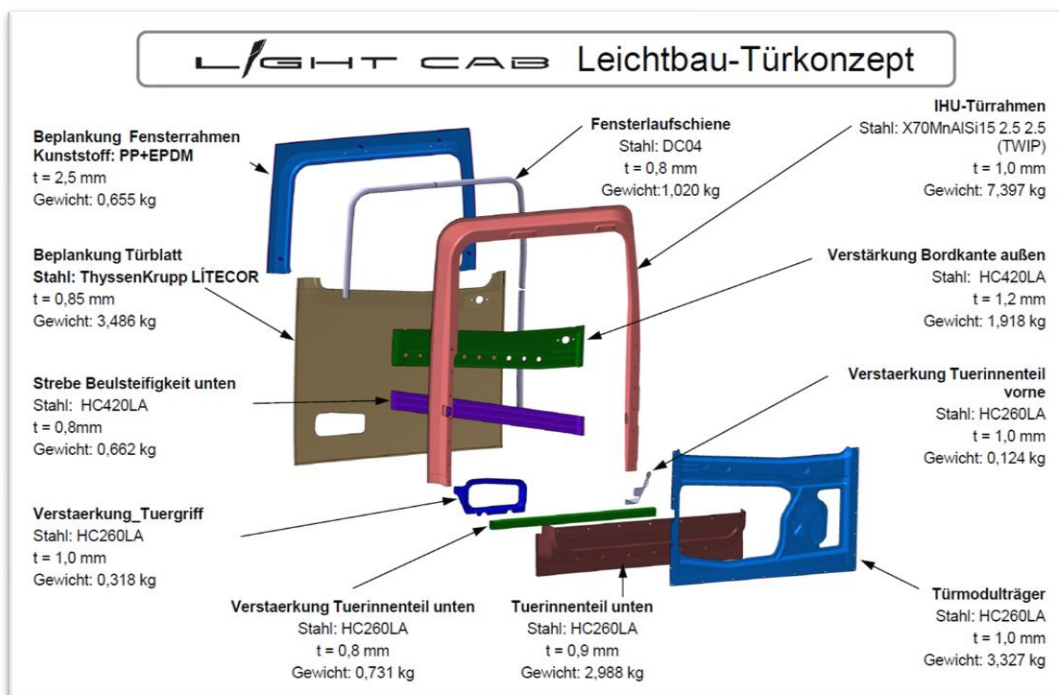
Ursprüngliche Planung: 9 Strukturteile mit 12 Werkzeugen
